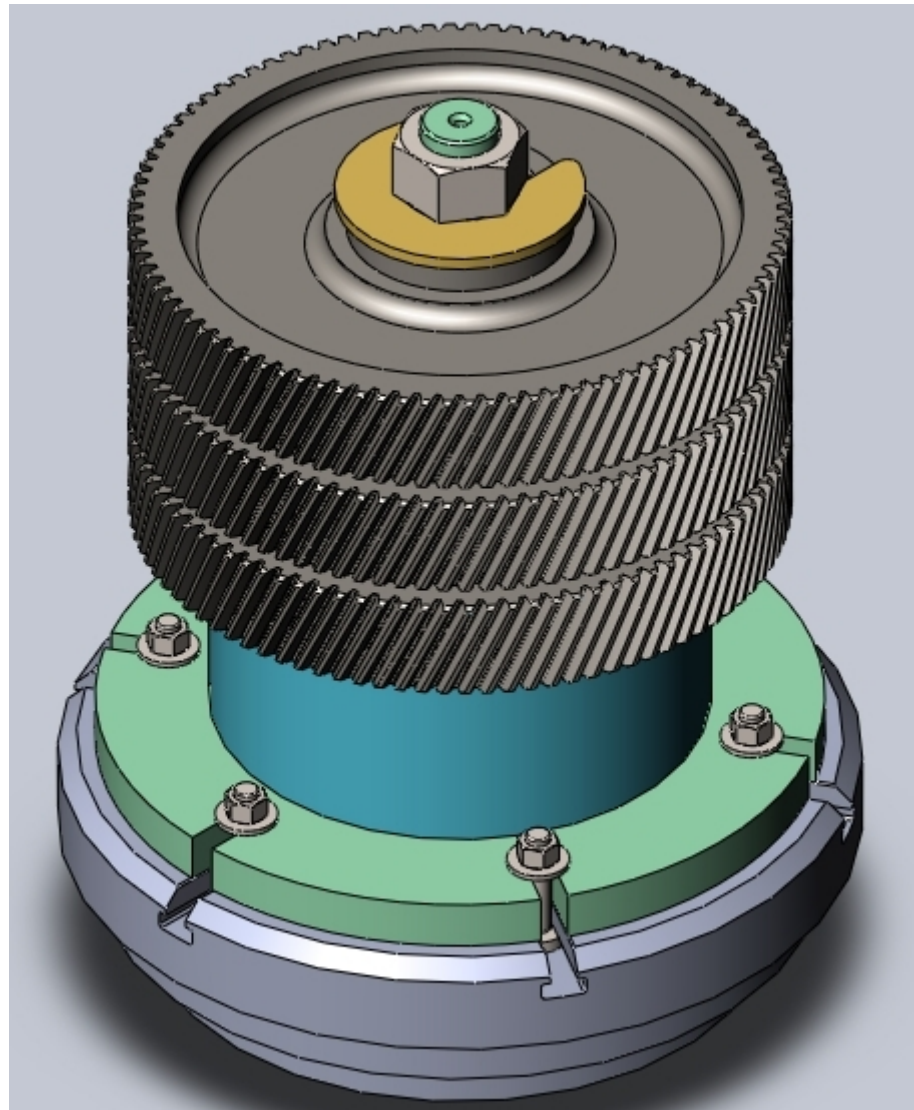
Пристрій фрезерний для нарізання зубців на поверхні 5
